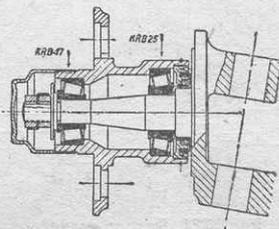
Ступица переднего колеса на конусных роликовых подшипниках.
